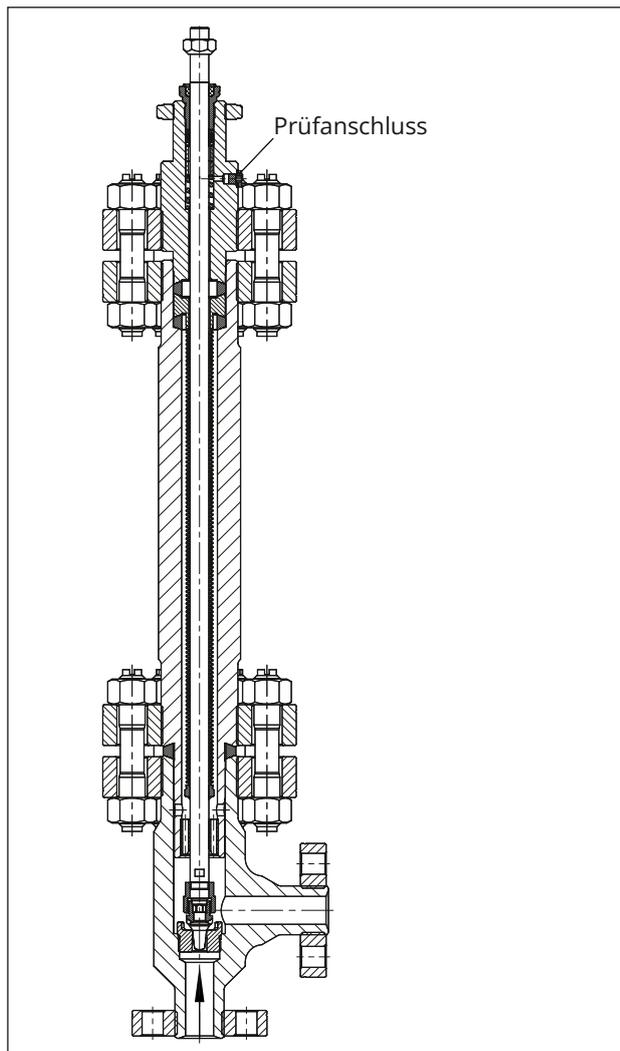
Ventil Typ 3259 mit Metallbalgabdichtung und Prüfanschluss
